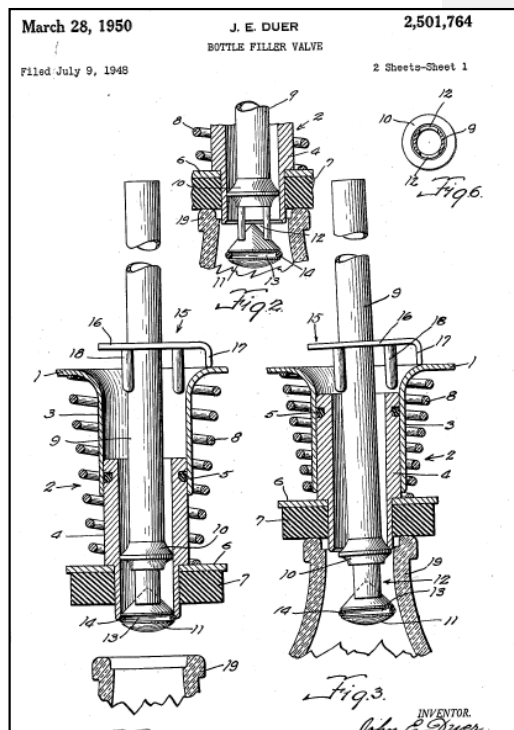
Bottle Filler Valve [ref \[26\]](#).
